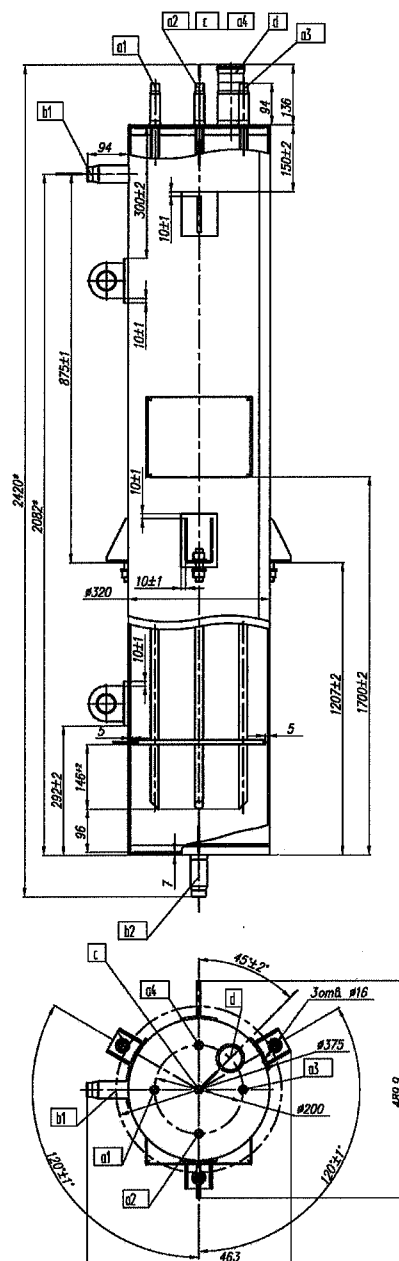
Габаритный чертеж бака-гидрозатвора KPL70BV001
